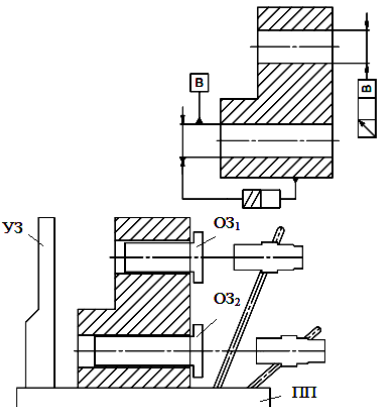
Схема контроля соосности отверстий корпусных деталей
